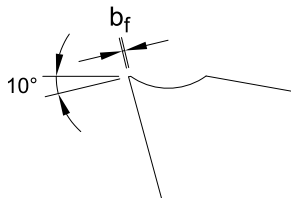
Záporný vrcholový úhel pro hrubování
